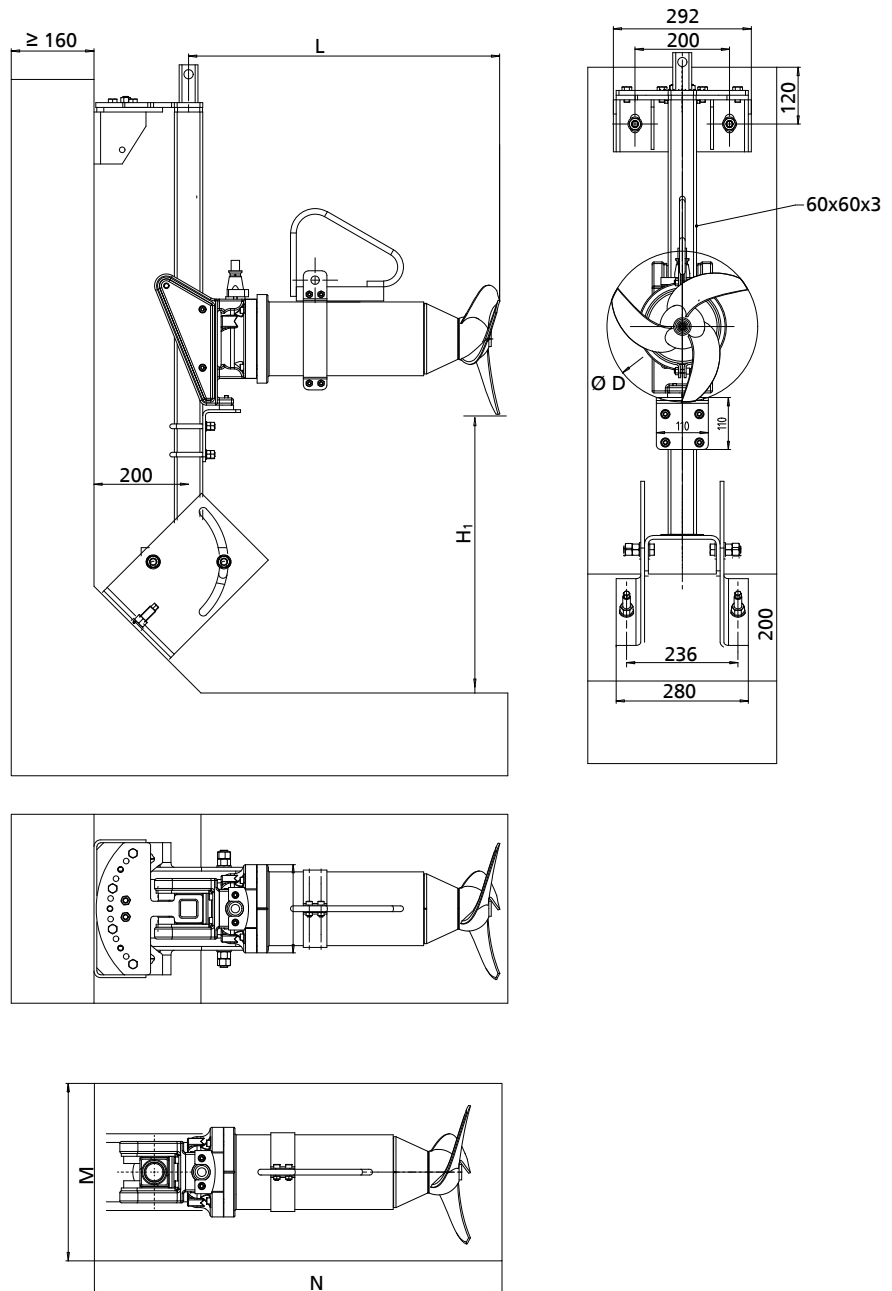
Установка принадлежностей 22 — Amatrix 200/300/400 (внешний типоразмер 4135)
